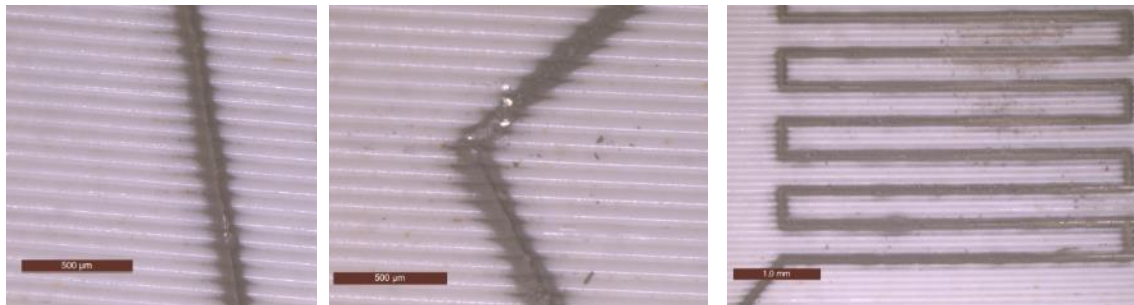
Pista depositada sobre pieza de PLA FDM zonas 1, 2 y 3
